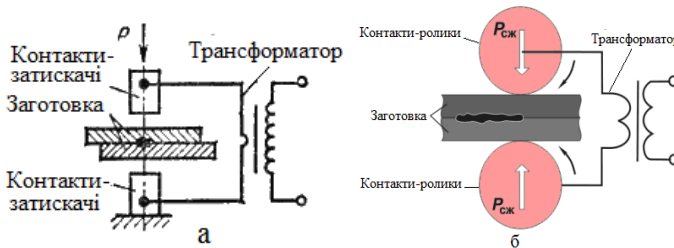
Схема точкового (а) та шовного (б) зварювання
